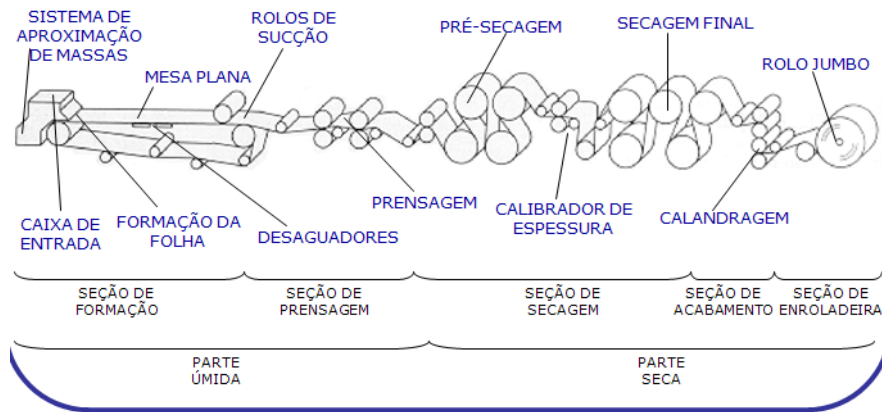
MÁQUINA DE FABRICAÇÃO DE PAPEL.
